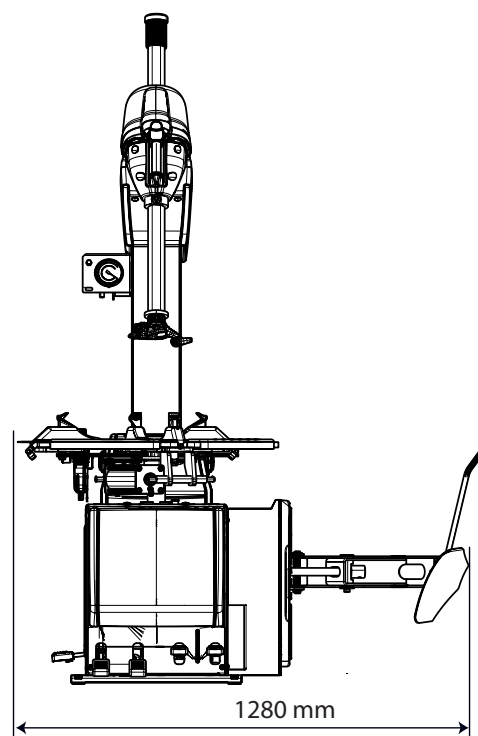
Dimensions de FALCO EVO 622/622 IT (vue de face)
